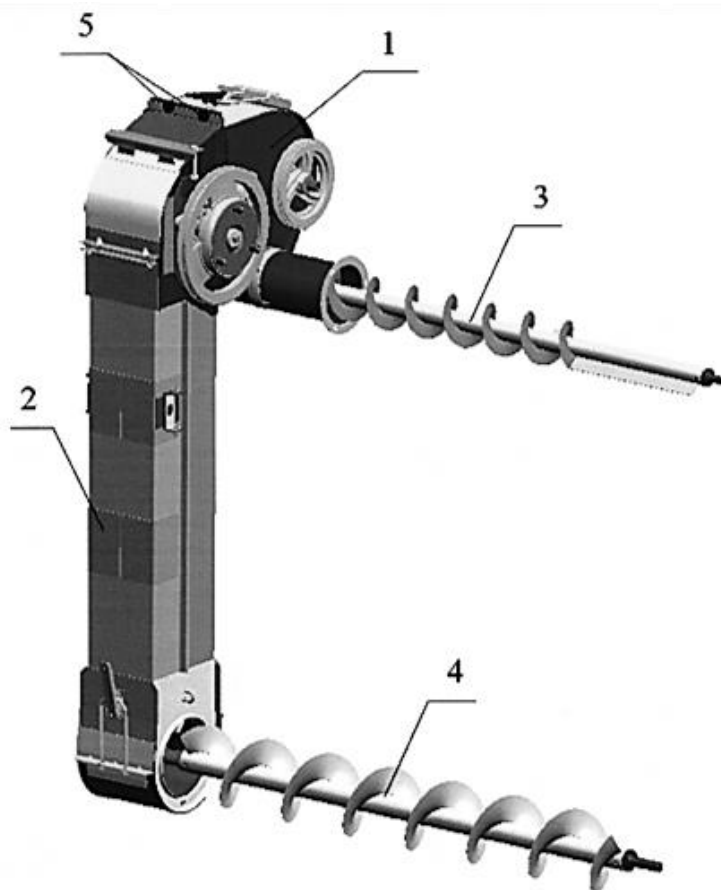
Общий вид домолачивающего устройства: 1 – домолачивающее устройство; 2 – колосовой элеватор; 3 – распределительный шнек; 4 – колосовой шнек; 5 – болтовое соединение
